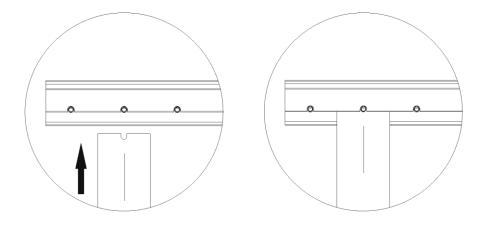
Einsetzen des mono Connector Boards, exemplarisch
